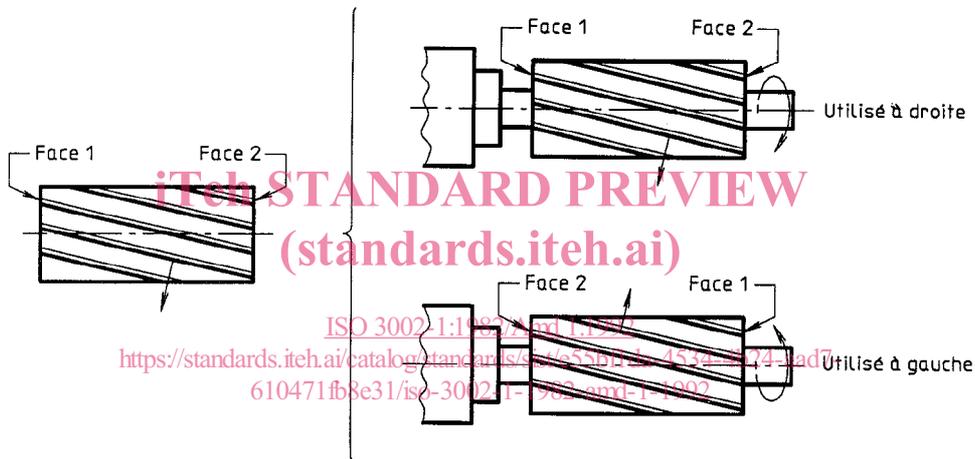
Outil cylindrique neutre (sens de coupe à gauche et à droite)
